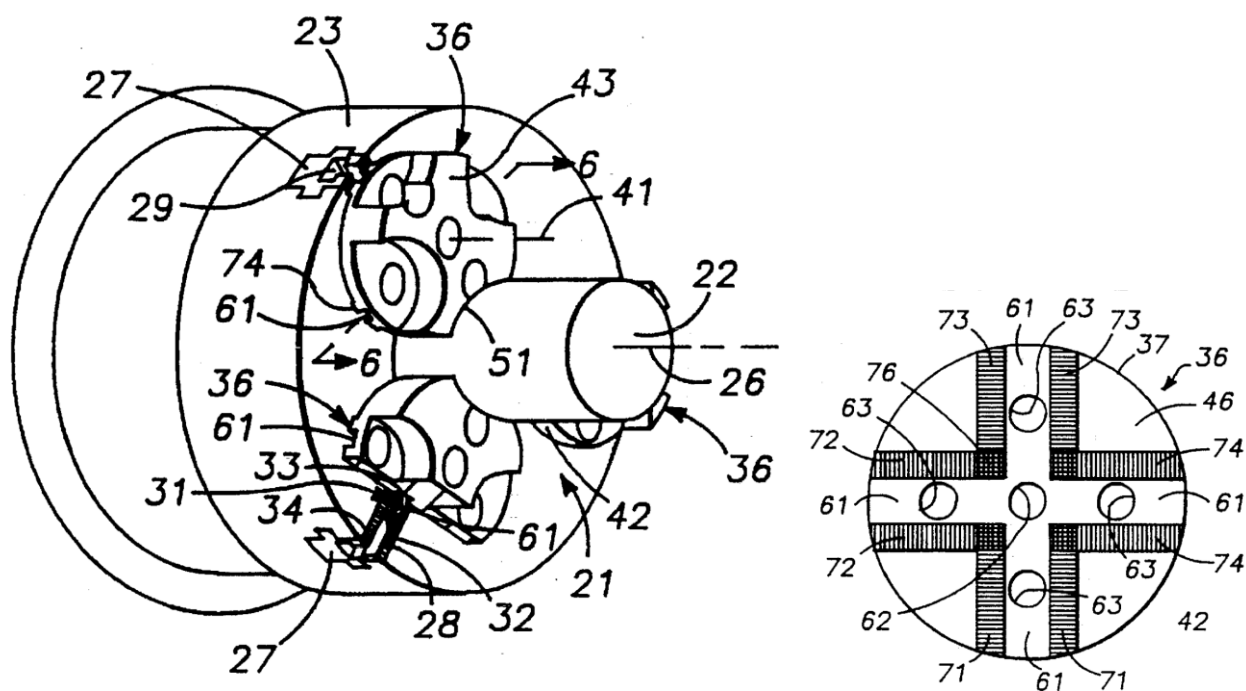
Токарний патрон із поворотними багатопрофільними затискними елементами циліндричного типу
